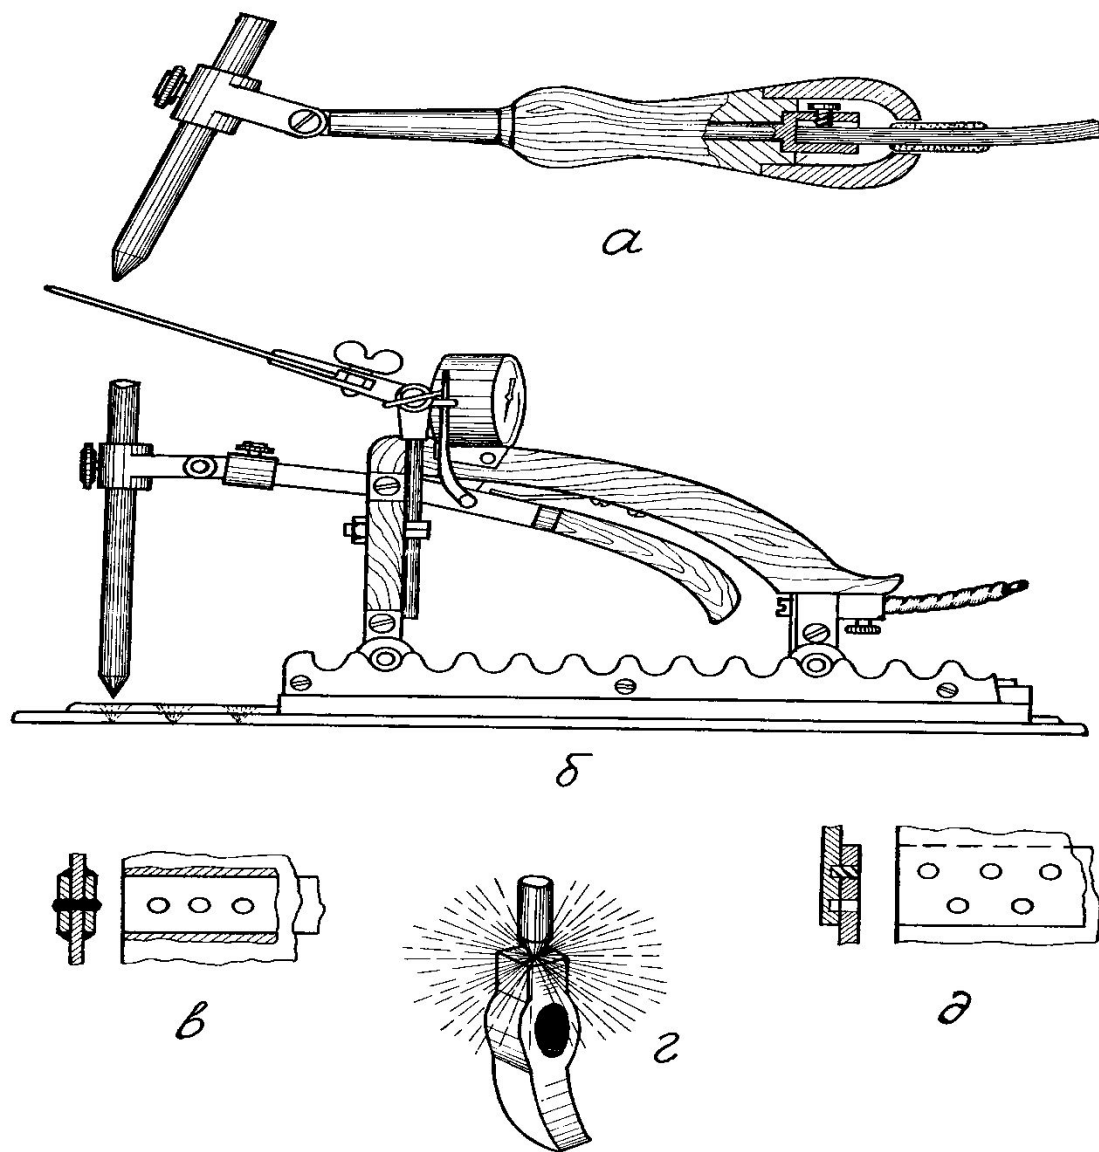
Некоторые чертежи к привелегии Н.Н.Бенардоса на изобретение «электрогефеста»: а – держатель для дуговой сварки; б – держатель для точечной дуговой сварки; в,д – нахлесточное соединение, полученное с помощью пробочных и фланговых швов; г – наплавка бойка молотка.
